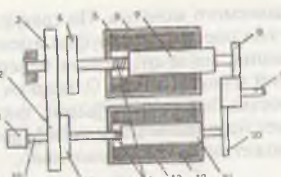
Муфта сухого трения: 1-ведущий двигатель; 2,3-шестерни; 4,15-фрикционные диски; 5,12-обмотки; 6,13-электромагниты; 7,11-якоря; 8,10-шестерни; 9-ведущий вал; 14-пружины; 16-ведущий вал.
